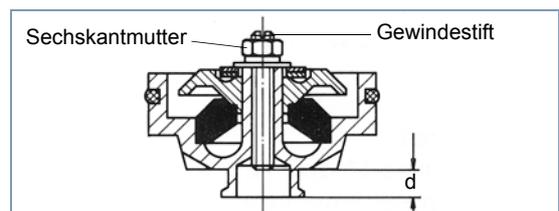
Maß d (Gerät mit einer Gummifeder)
